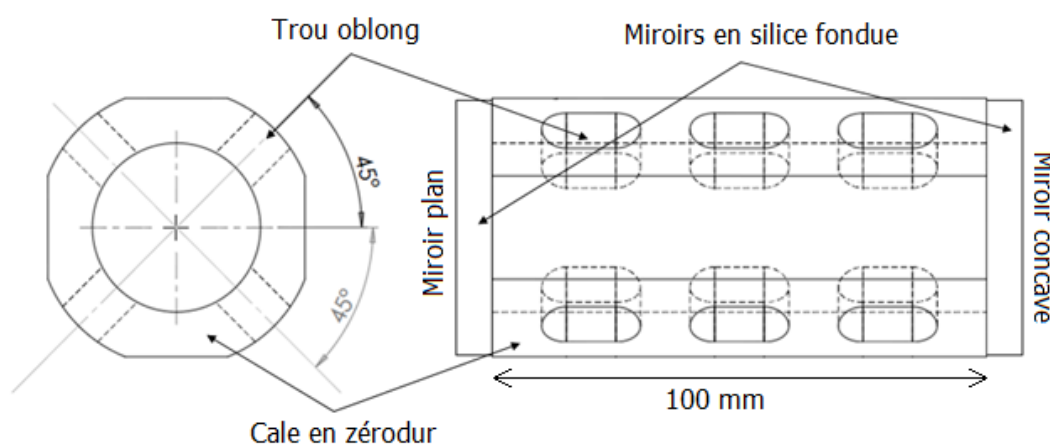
Plan de la cavité Fabry – Pérot en zérodur (coupe longitudinale et transversale)
